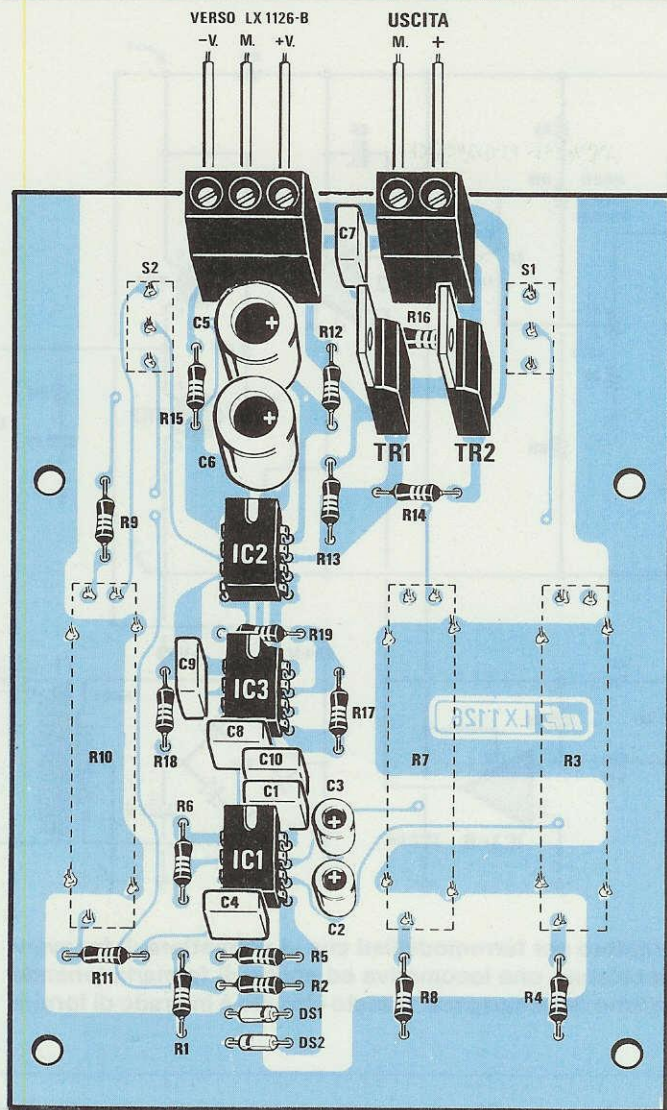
Schema pratico di montaggio dello stampato LX.1126 visto dal lato in cui dovrete montare la maggior parte dei componenti. Sul retro dello stampato monterete i componenti visibili in fig.13.
